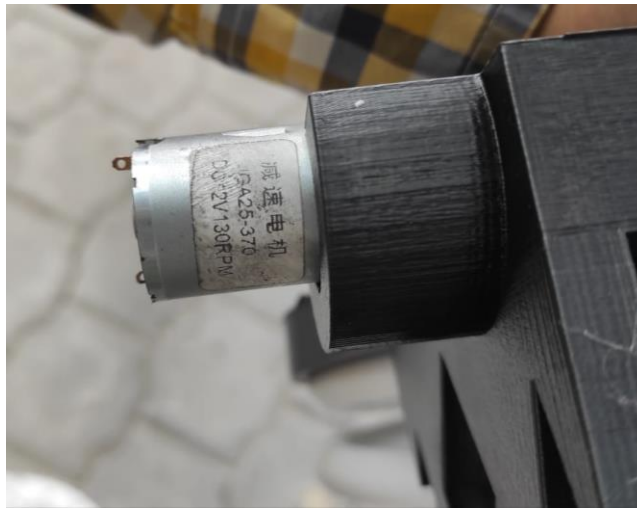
Cubierta superior modificada impresa en 3D vista I.
